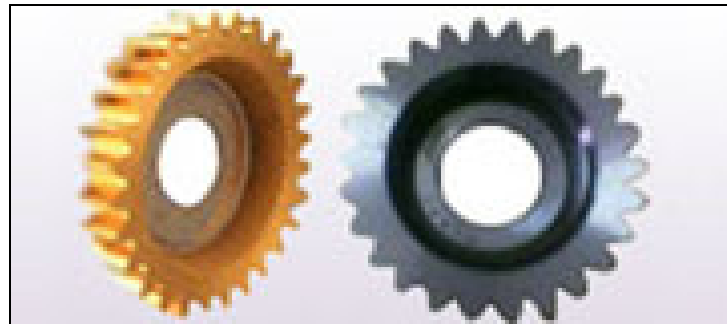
Ferramenta de corte de dentes retos (Shaper)
